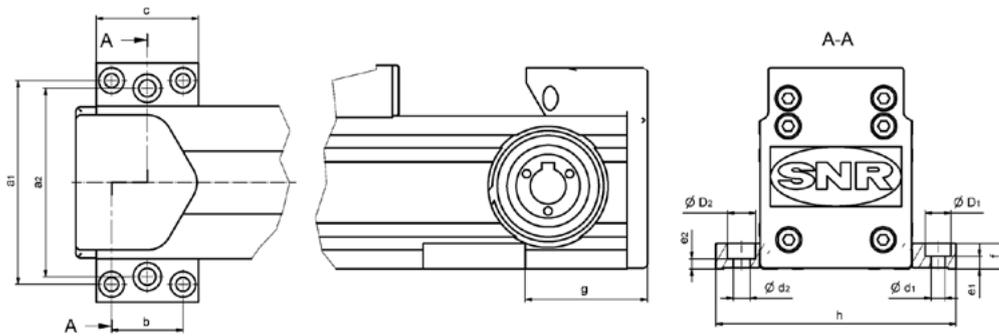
Abmessungen Befestigungsleisten AXC / AXDL
